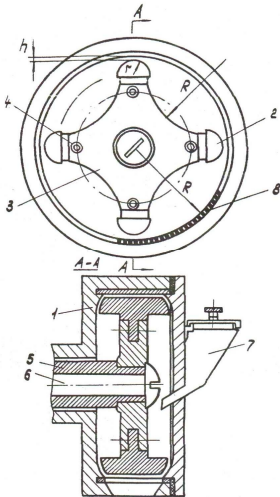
Схемы камеры роторного овализатора: 1 – корпус; 2 – биды; 3 – ротор; 4 – пальцы крепёжные; 5 – втулка; 6 – вал; 7 – питатель; 8 – загрузочная решетка
